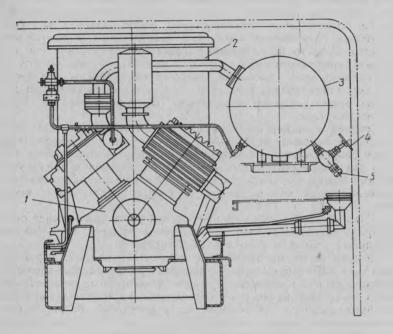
Компрессорная установка автомобиля AT-2 (157K) 1 — компрессор; 2 — холодильник; 3 — воздухосборник; 4 — вентиль; 5 — ниплель
